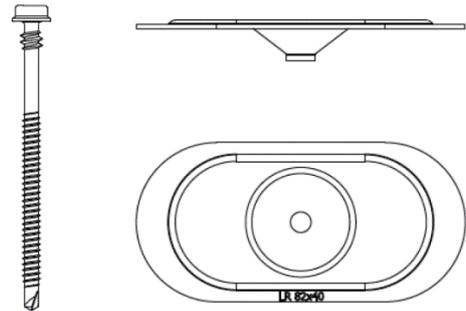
Vis ETANCO EHB DF-2C 4.8 + plaquette de fixation ETANCO DVP DF 8240R
